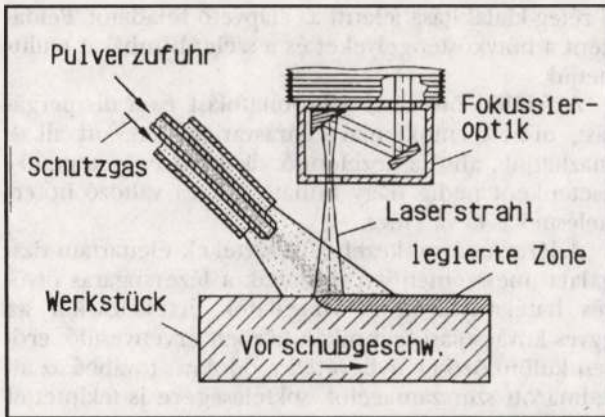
Laserstrahllegieren von Schmiedewerkzeugen
